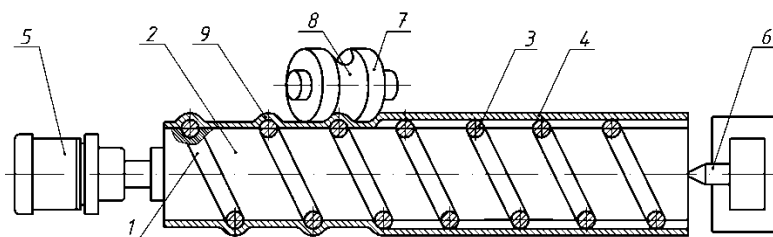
Конструктивна схема способу виготовлення гвинтової поверхні транспортної труби
